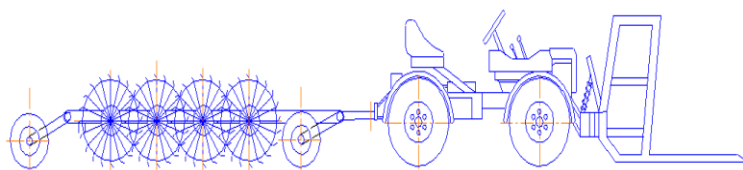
Схема комбинированного малогабаритного агрегата для уборки сена
